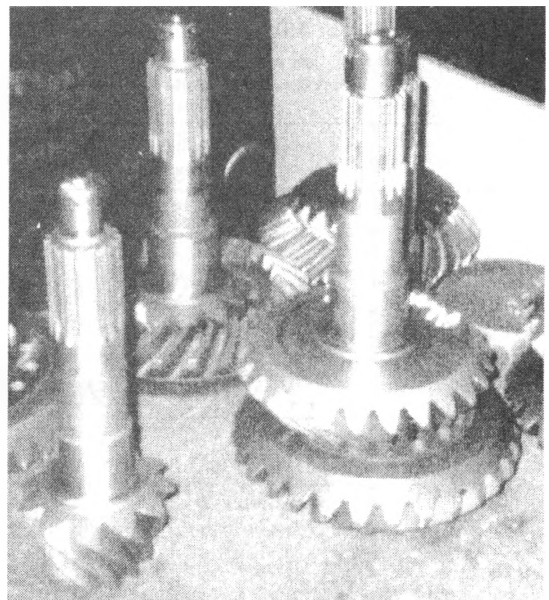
Шестерни главной передачи заднего моста автомобиля МАЗ-5551, изготовленные из бейнитного высокопрочного чугуна
